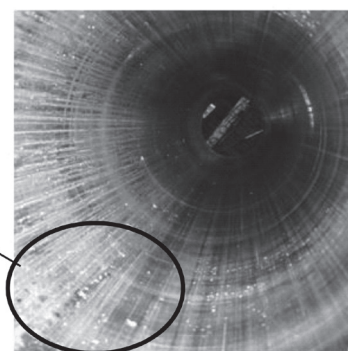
Царапины и следы коррозии на поверхности гильзы гидроцилиндра
